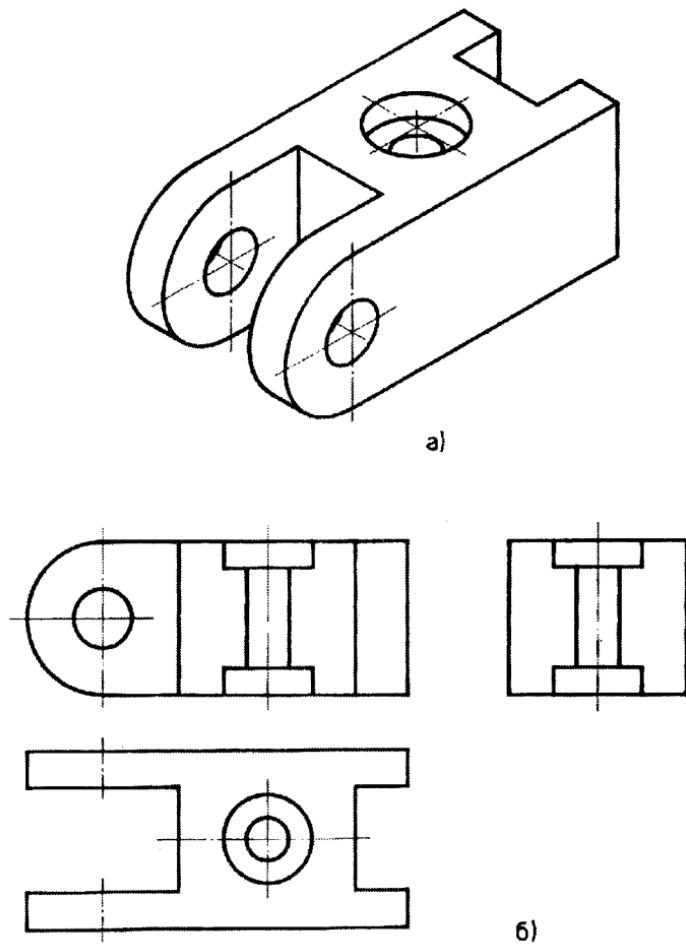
Наглядное изображение и частично выполненный чертеж детали
